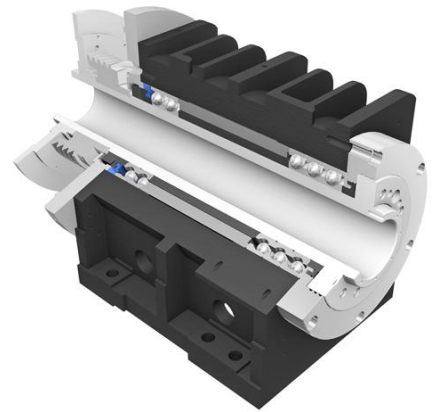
Корпус шпиндельной бабки станка с ЧПУ WIA Machine Tool L230LMSA (Корея)
